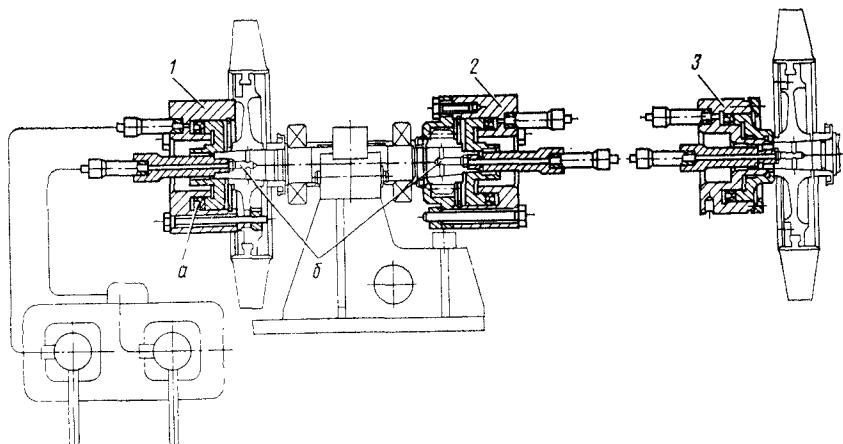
Приспособления для спрессовки и напрессовки колеса и шестерни ротора вентилятора:
